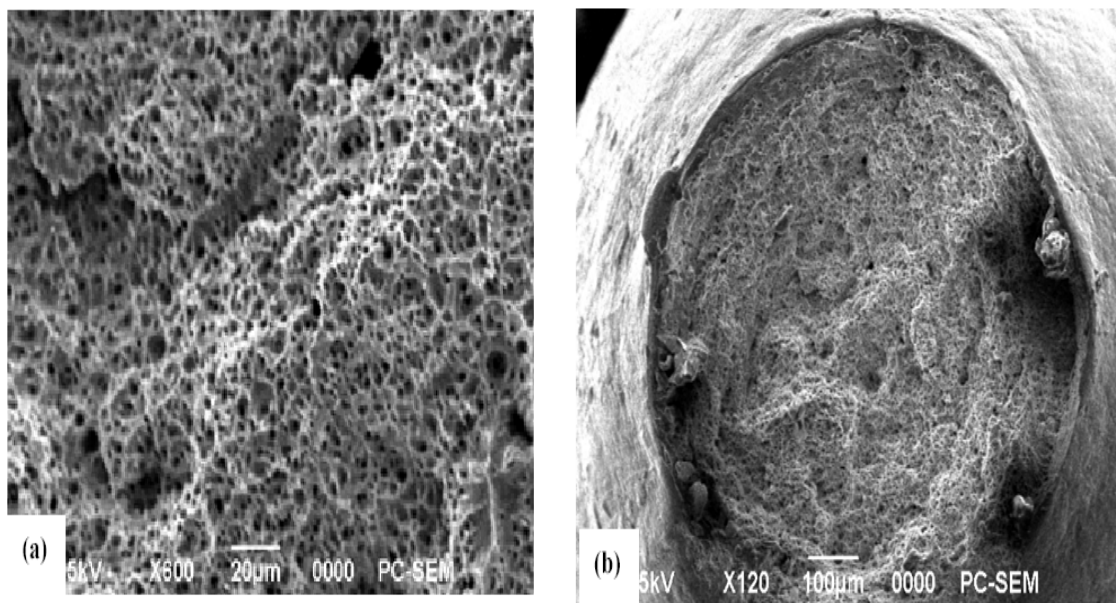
Fractographies des surfaces fracturées d'un fil d'aluminium tréfilé à taux de réduction 96.41 % et flué sous 144 MPa à 160 °C (a) : fort agrandissement (x600) ; (b) : faible agrandissement (X120) [31].
